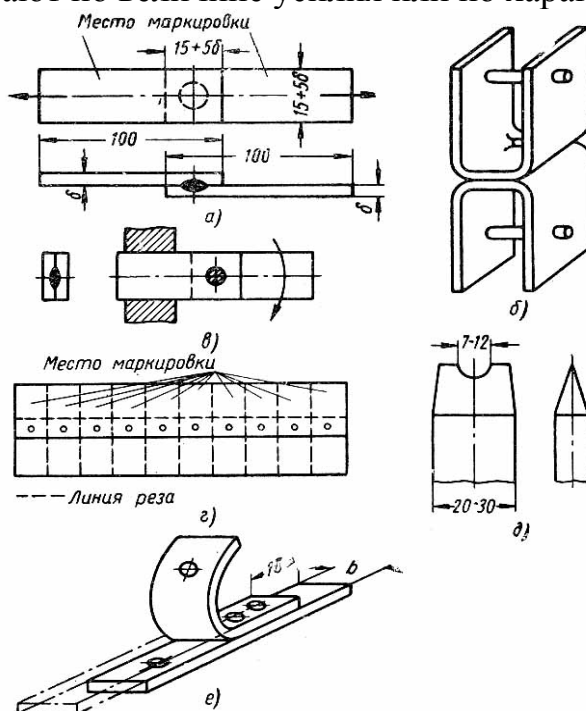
Образцы для испытания точечной сварки
